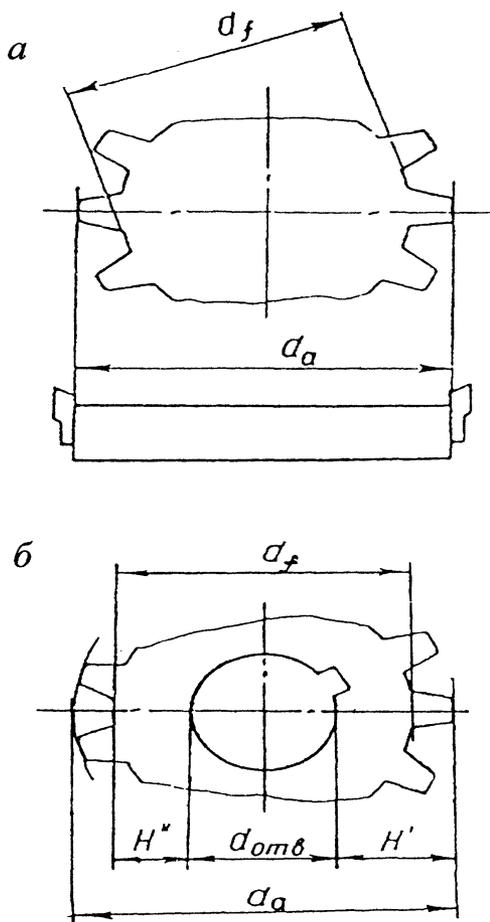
Схема обмера диаметров вершин (d_a) и впадин (d_f) зубчатого колеса:
